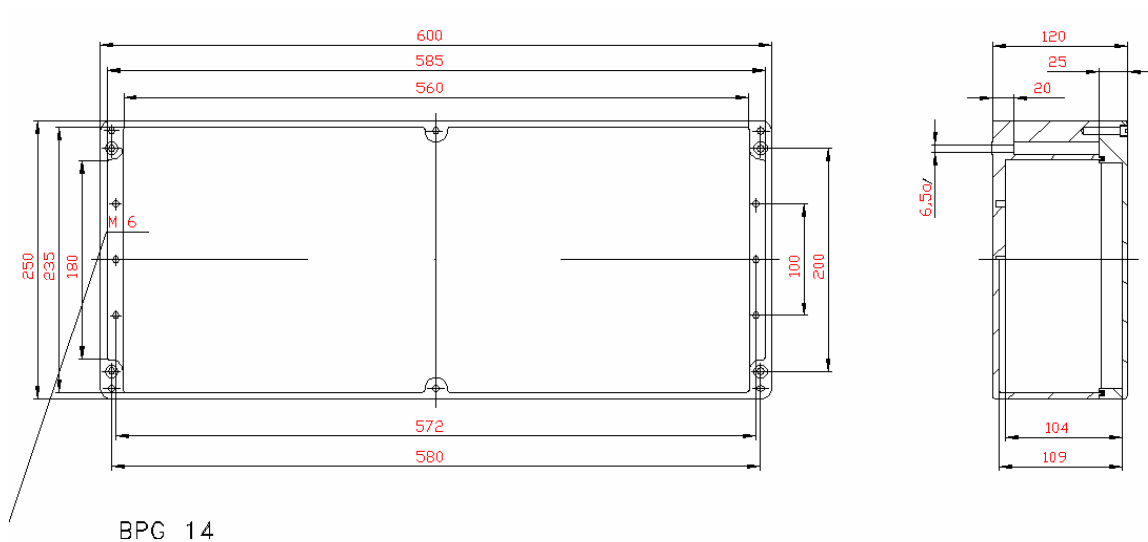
1: Kunststoff-Gehäuse IP67 für die Motorsteuerung
